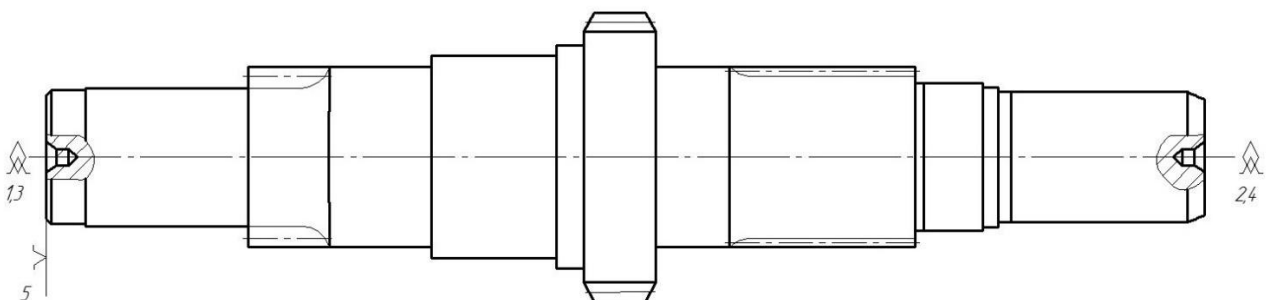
Схема вторинного валу КПП FORD Explorer.
